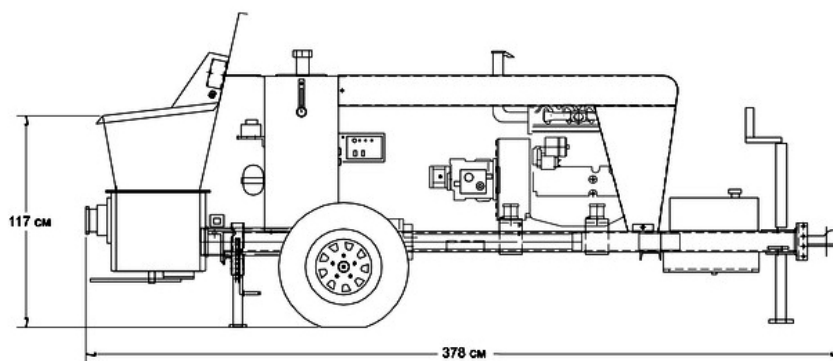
Čerpadlo betonu Schwing SP 305
